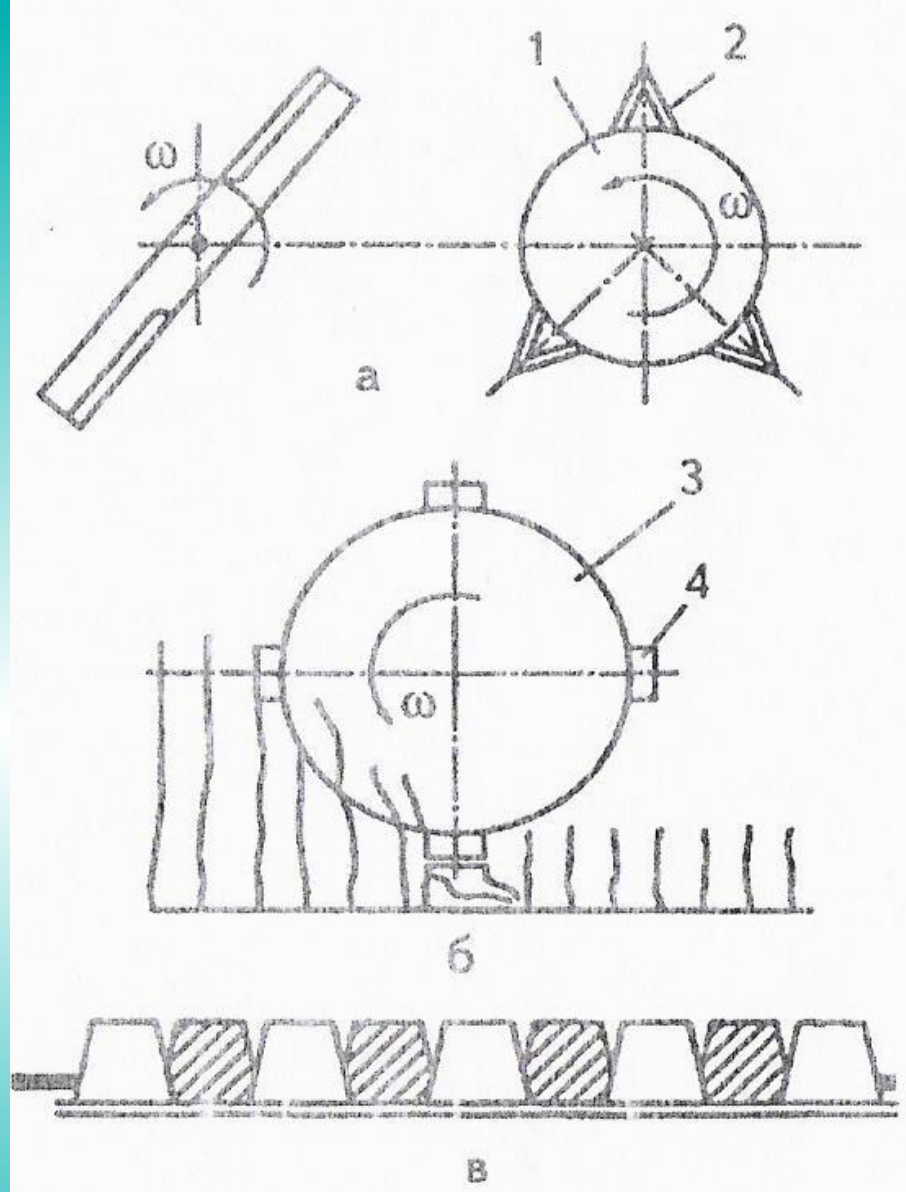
Схемы режущих аппаратов: а - плосковращательный режущий аппарат; б – вращательно-цилиндрический аппарат; в – аппарат с возвратно-поступательным движением режущих элементов: 1 – ротор; 2 – нож; 3 – барабан; 4 – спиральный режущий нож; ω – угловая скорость режущего элемента
